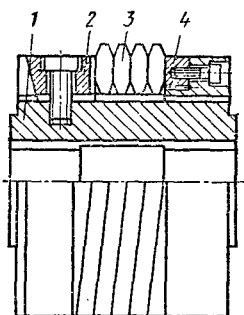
Червячная фреза с твердосплавными поворотными зубьями (пластинками)
